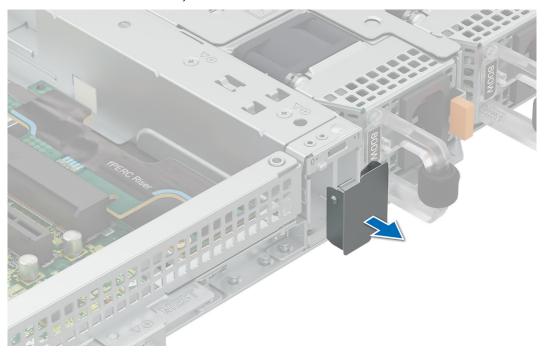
Entfernen des Platzhalters für das BOSS-N1-Modul
